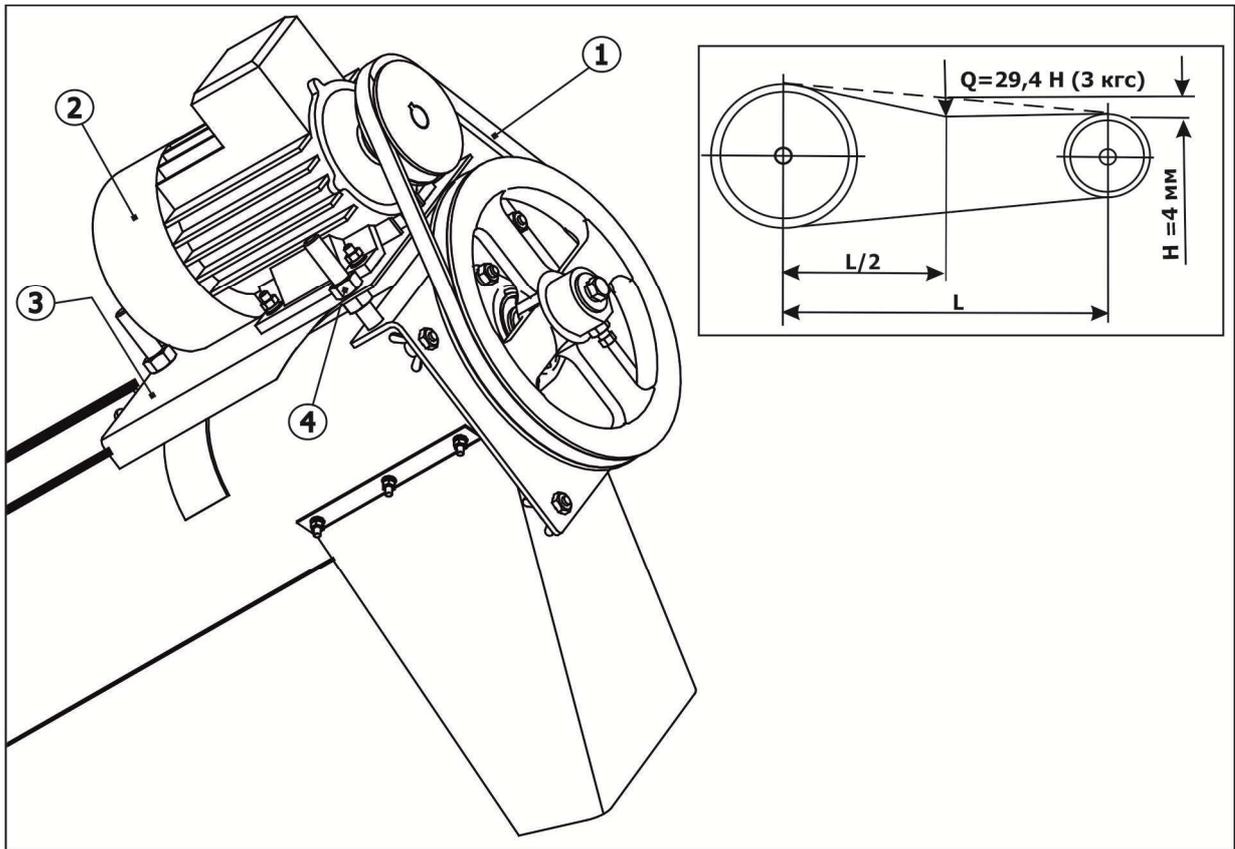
Регулировка натяжения клиноременной передачи привода приставки
